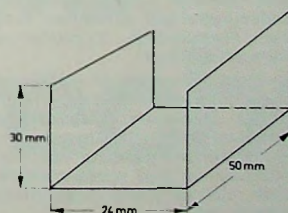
Maßzeichnung des Kühlkörpers (Cu- oder Al-Blech, 1,5 mm)
